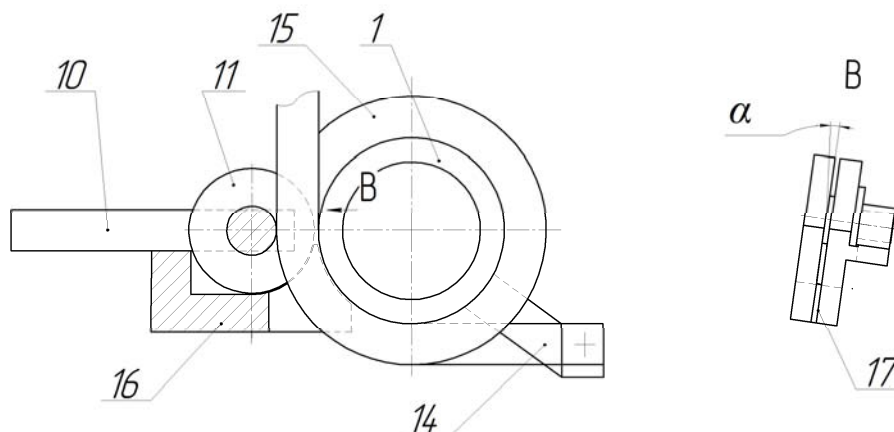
Конструкція ролика із додатковою державкою для навивання стрічкових гвинтових робочих органів
